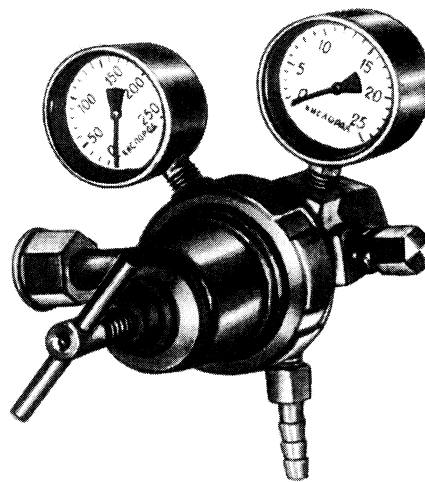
Баллонный двухступенчатый редуктор ДКД-8-65
